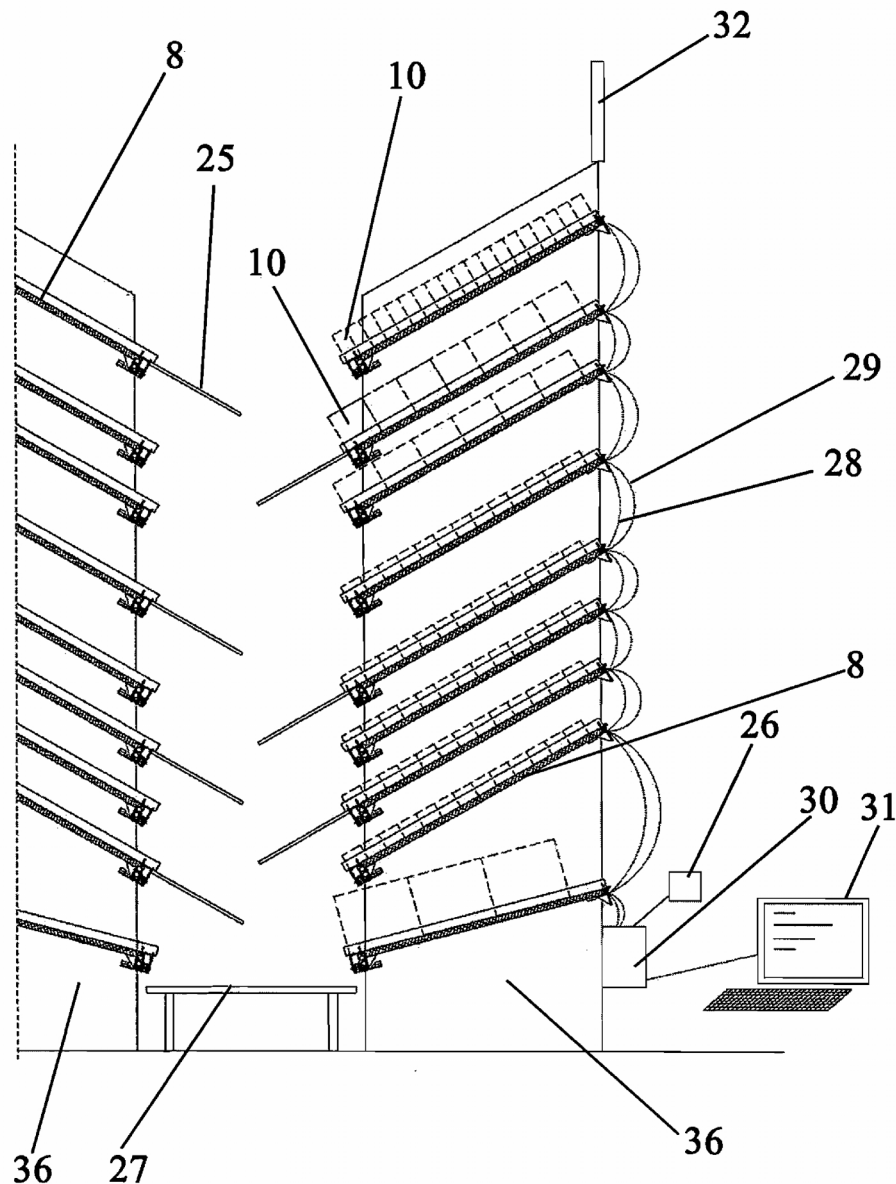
Vista de perfil de la instalación con las rampas de frenado.
